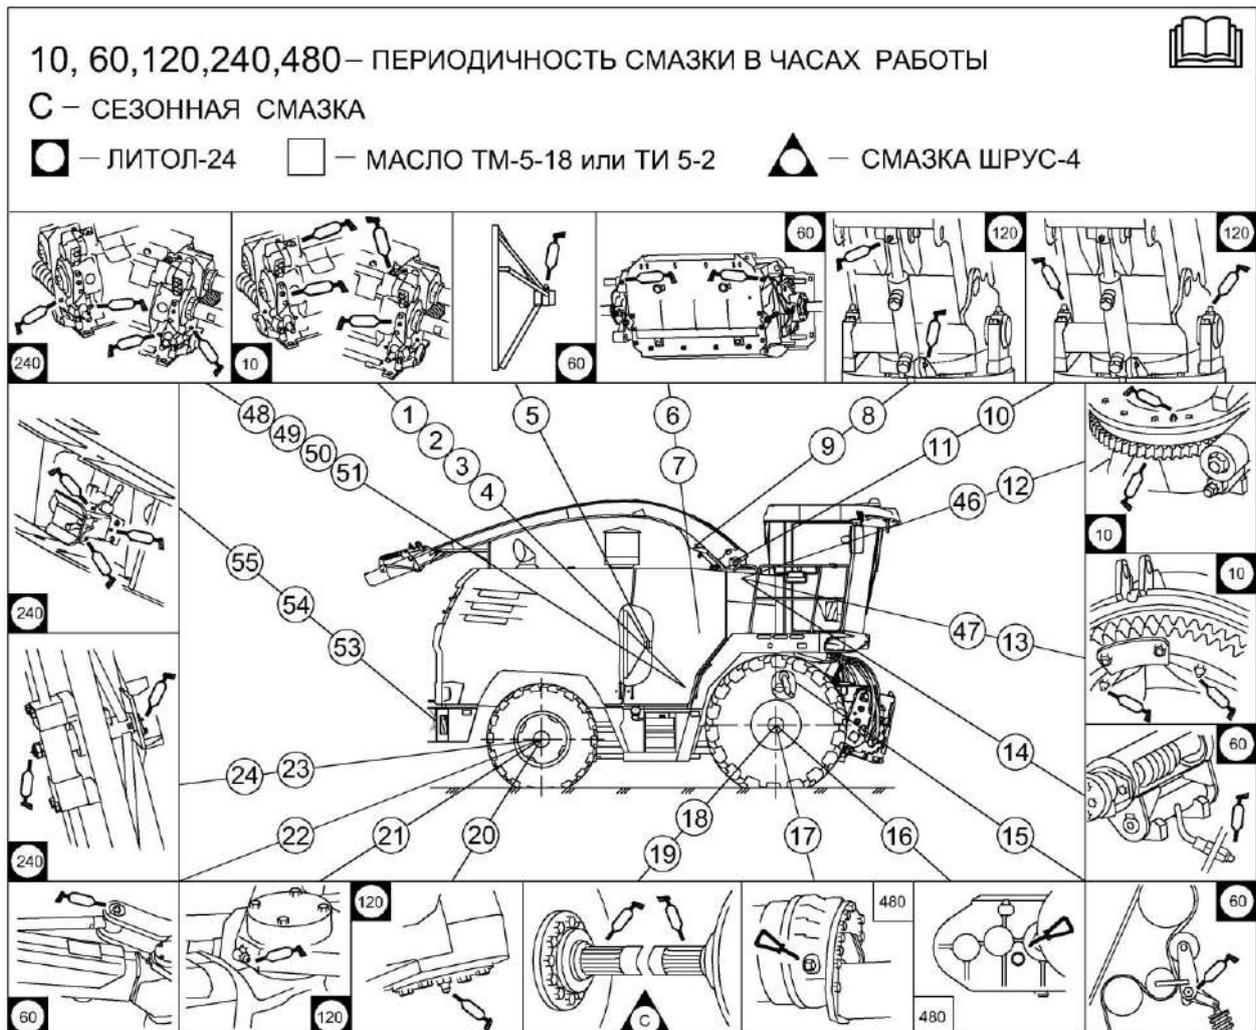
Схема смазки комбайна (вид справа)
